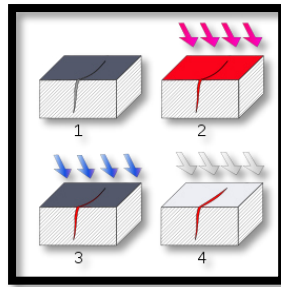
Proceso general de inspección por líquidos penetrantes 1. Corte de un material que presenta una grieta .2. La superficie del material se cubre con penetrante. 3. Se elimina el exceso de penetrante. 4. Se aplica el revelador, volviéndose visible el defecto.
